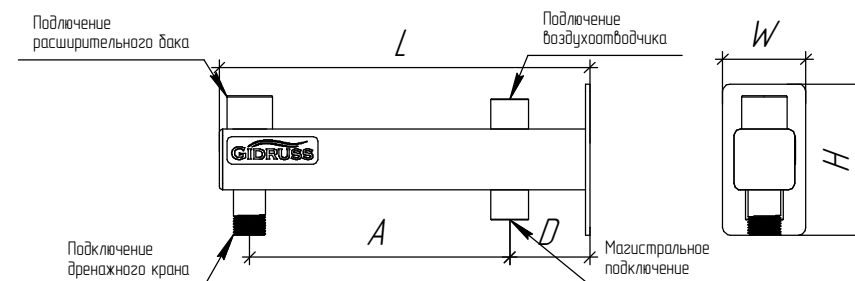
Габаритно-присоединительные размеры основания консоли для расширительного бака BKSS-18U.BASIS
